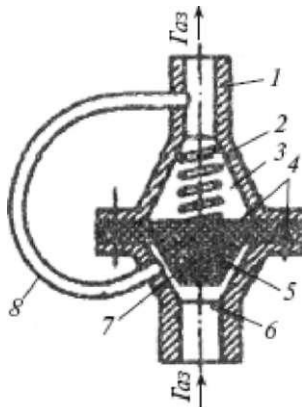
Сухой мембранный предохранительный затвор ЗСН-1,25: 1 - корпус; 2 - пружина; 3 - взрывная камера; 4 - мембрана; 5 - коническое утолщение мембраны; 6 - газоподводящий коллектор; 7 - седло; 8 - петлевой трубопровод
